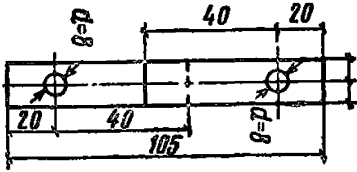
Схема сверления стандартного образца для испытания на сдвиг при растяжении
